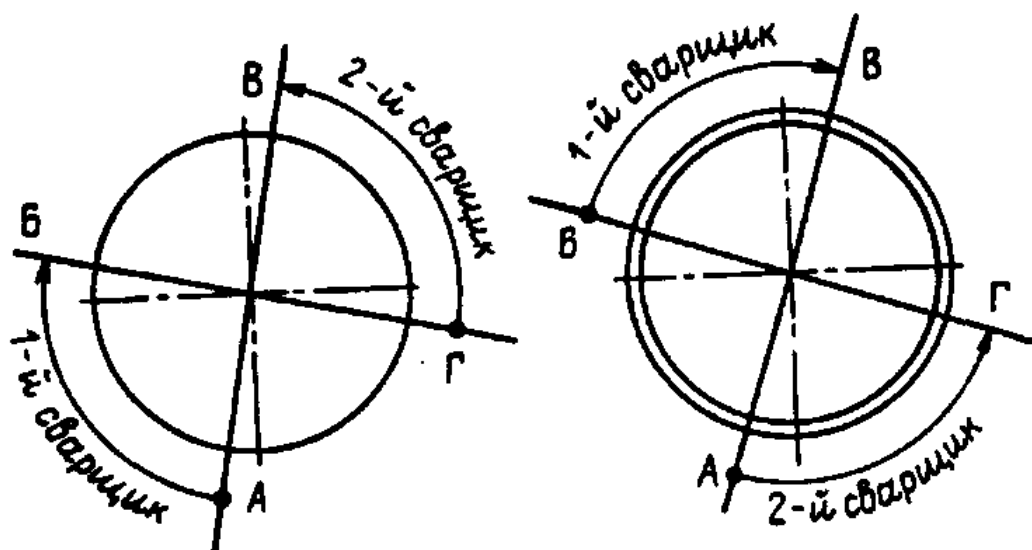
Порядок наложения первого слоя шва при сварке двумя сварщиками вертикальных неповоротных стыков труб диаметром 219 мм и более
